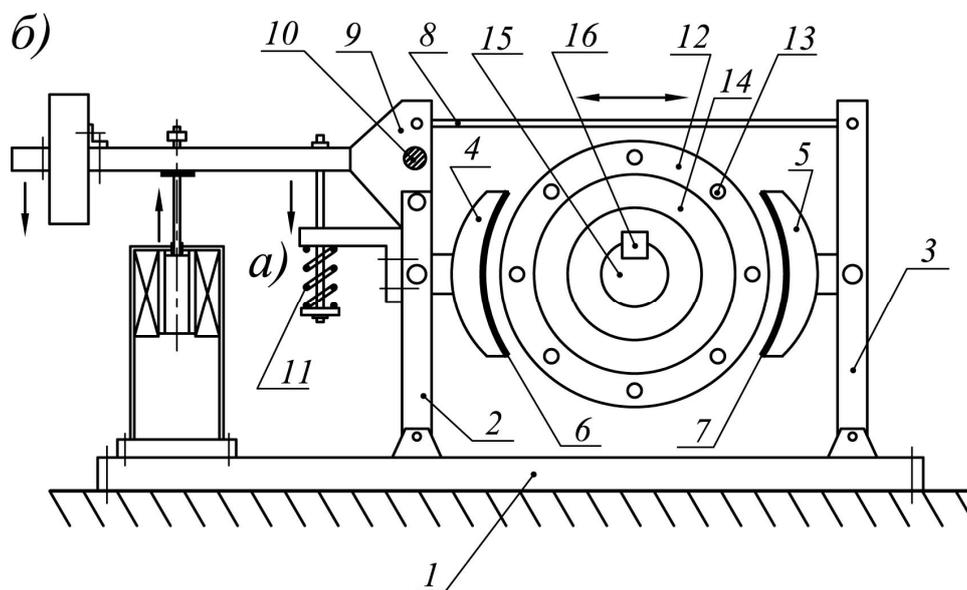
Колодочный электромагнитный тормоз с пружинным а) и рычажным б) приводами:
